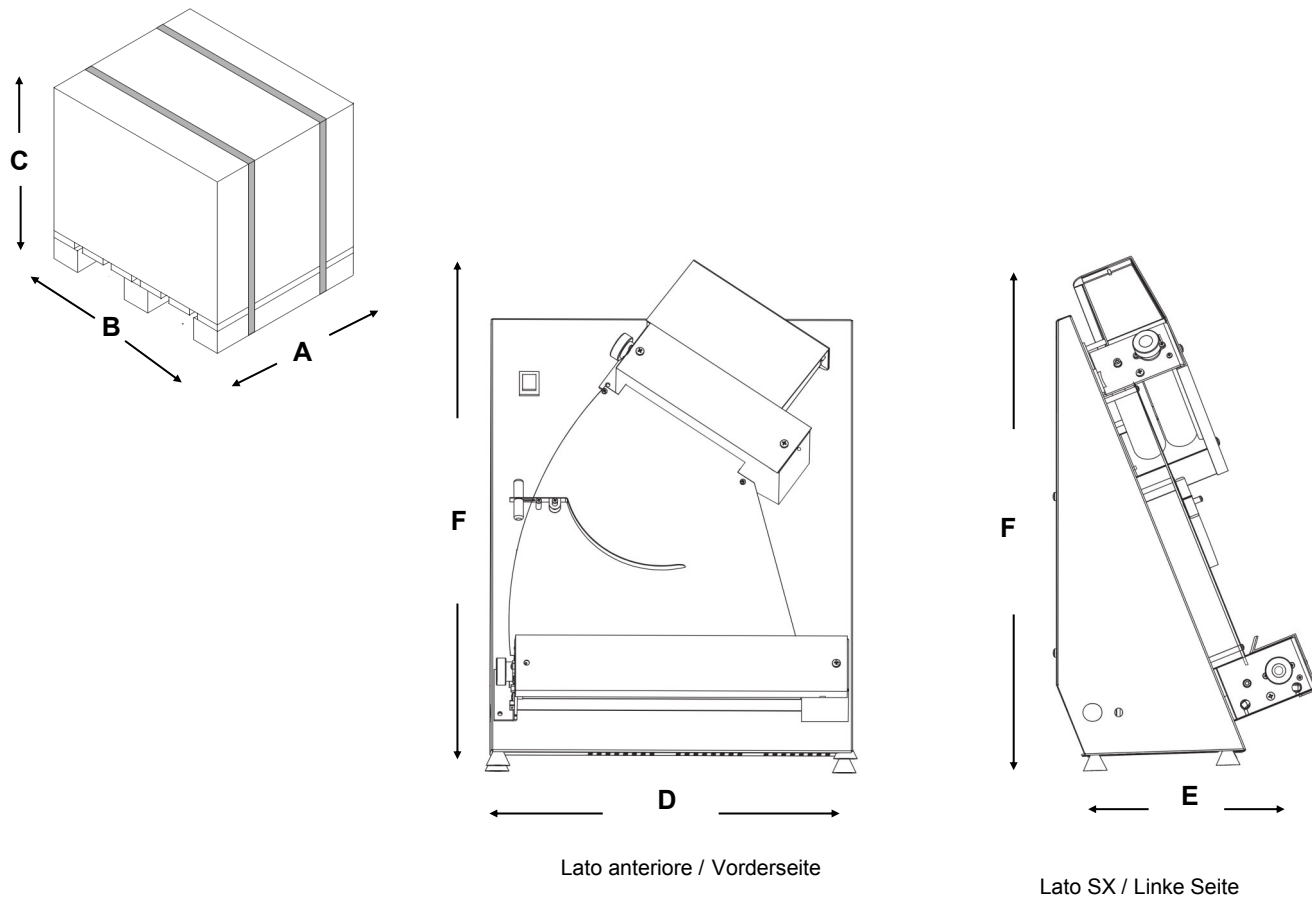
(Dimensioni della stendipizza) / (Maschinenabmessungen)
